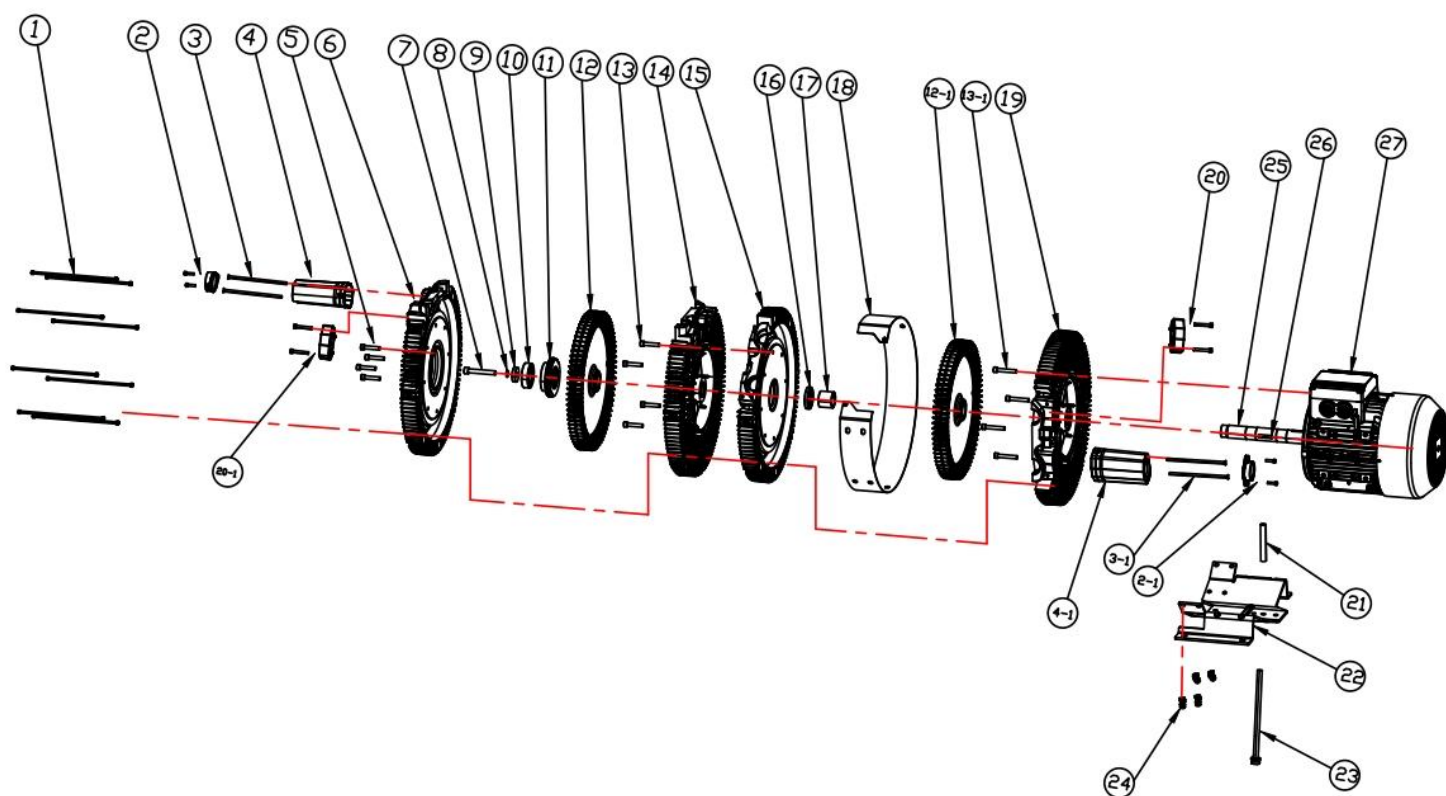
Деталировка трехступенчатых воздуходувок 4RB
